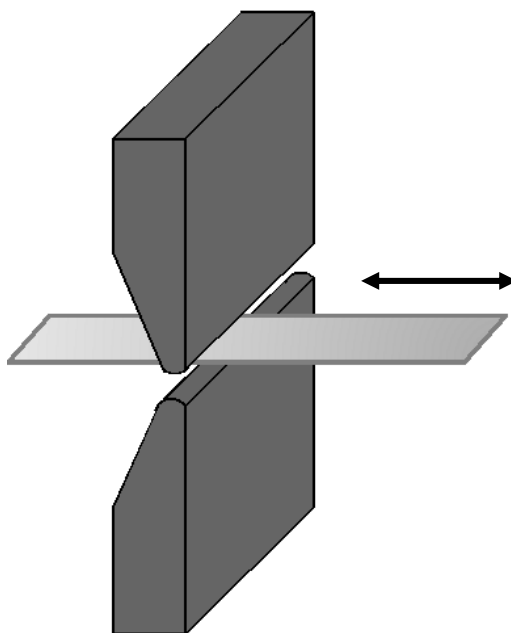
Схема расположения инденторов при поверхностном деформировании стали ЗИ-126
